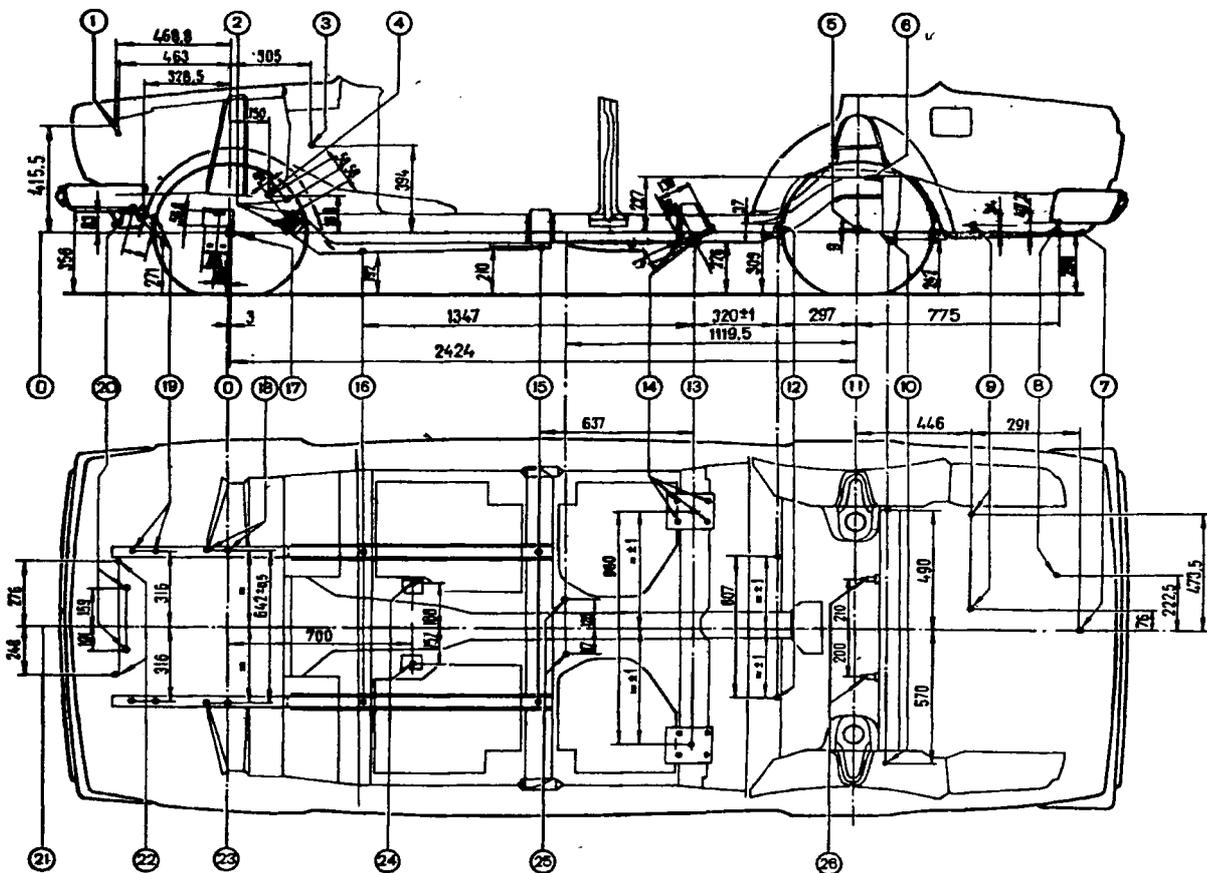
Точки крепления узлов шасси: 0 - базовая линия; 1 - верхнее крепление радиатора; 2 - крепления картера рулевого механизма и маятникового рычага; 3 - ось педалей сцепления и тормоза; 4 - центр рулевого механизма; 5 - центр заднего колеса; 6 - крепление амортизаторов задней подвески; 7 - центр заднего технологического отверстия центрального усилителя пола багажника; 8 - заднее крепление глушителя; 9 - переднее крепление глушителя; 10 - крепление поперечной штанги задней подвески; 11 - ось задних колес; 12 - оси болтов крепления верхних продольных штанг задней подвески; 13 - оси болтов крепления нижних продольных штанг к кронштейнам кузова; 14 - крепление кронштейнов нижних продольных штанг; 15 - центр заднего технологического отверстия переднего лонжерона; 16 - технологического отверстия переднего лонжерона; 17 - центр колеса; 18 - точки крепления поперечины передней подвески; 19 - крепление стабилизатора поперечной устойчивости; 20 - нижнее крепление радиатора; 21 - ось автомобиля; 22 - верхнее крепление радиатора; 23 - ось передних колес; 24 - крепление задней подвески двигателя; 25 - крепление опоры карданного вала; 26 - крепление амортизаторов задней подвески
